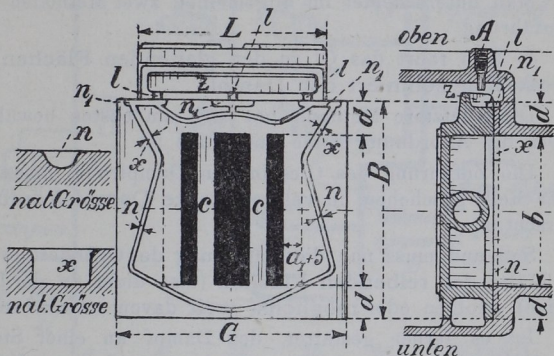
603. Nuten. Fig. 604. Grundriss. Fig. 605. Querschnitt.
